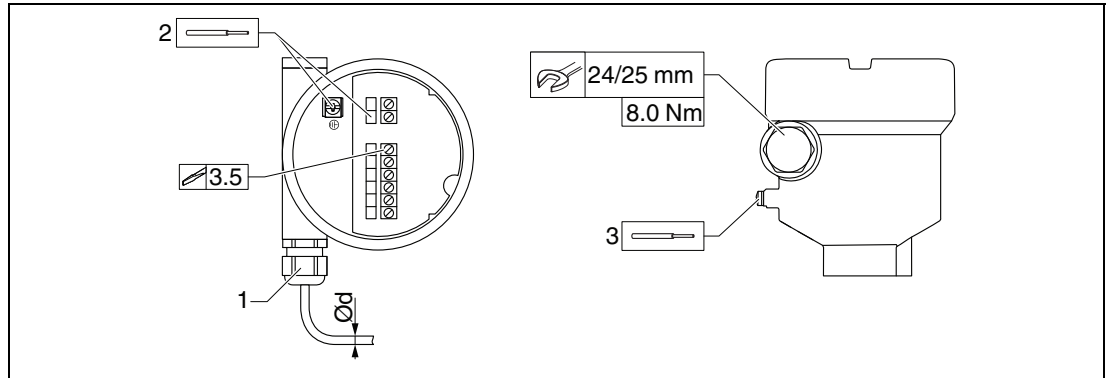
Beispiel Verschraubung mit Kabeldurchführung, Elektronikeinsatz mit Anschlussklemmen
